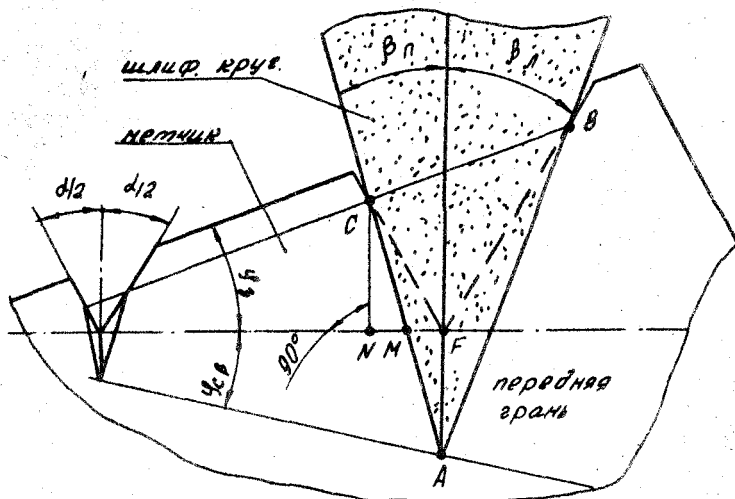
Способ изготовления с угловым смещением шлифовального круга
